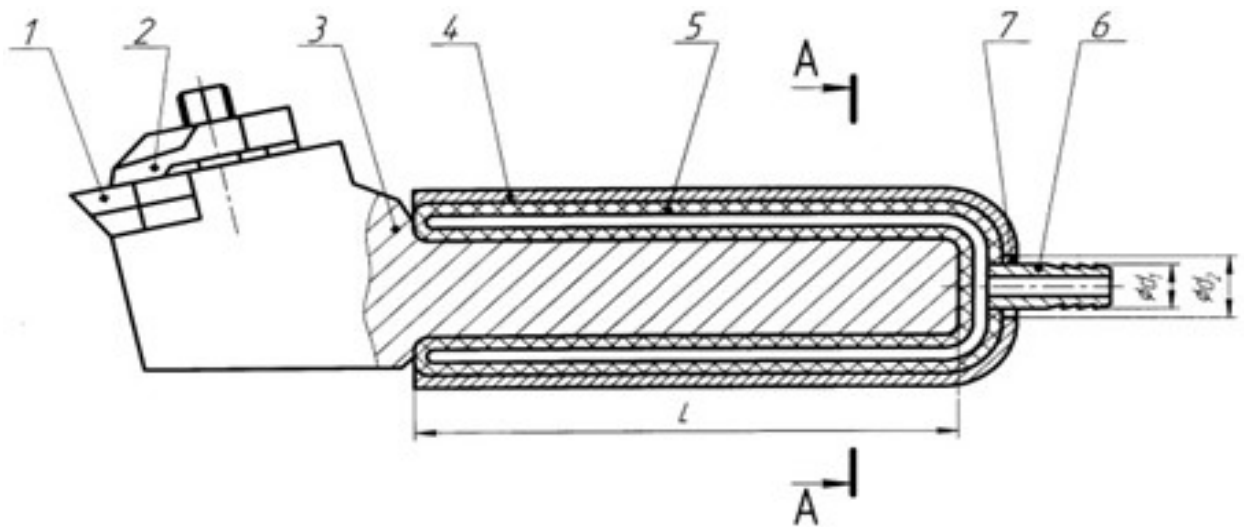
Механізм демпфування з множиною обтяжувальних елементів (1- ріжуча пластина, 2- кріплення, 3- державка, 4- металева склянка, 5- еластична оболонка, 6- циліндричний штуцер, 7- отвір)
